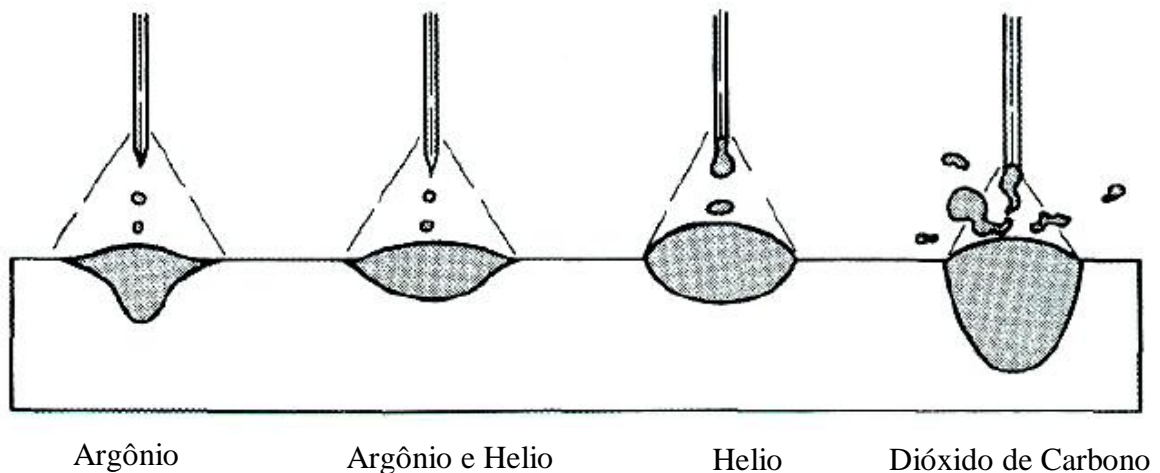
Perfil do cordão e penetração com diferentes tipos de gás (Welding Handbook, 2008).
